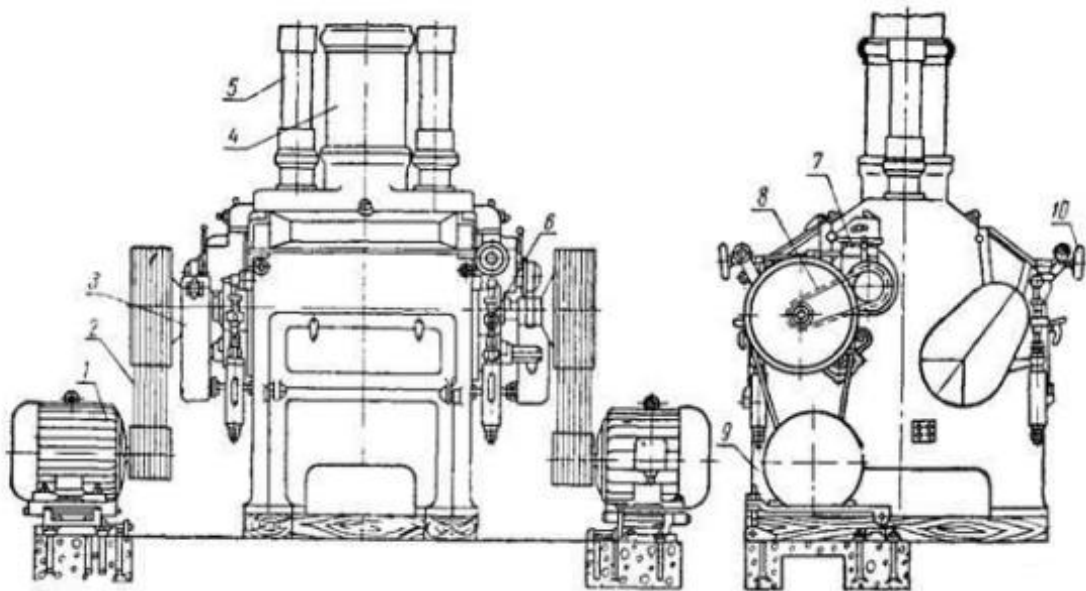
Вальцевий верстат БВ: 1 – електродвигун; 2 – клинопасова передача; 3 – коробка передач; 4 – приймальна труба; 5 – пневмопривід; 6 – механізм налаштування валів; 7 – автомат привально-відвальний; 8 – пасова передача; 9 – станина; 10 – механізм точного налаштування зазору вальців
